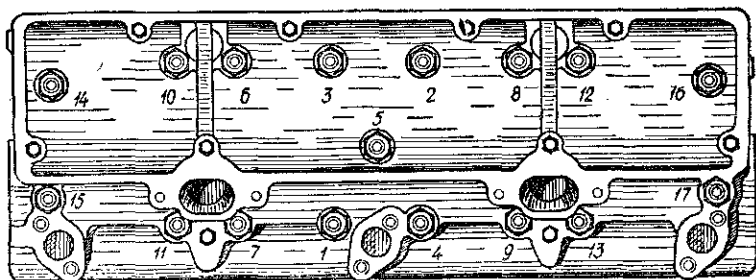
Порядок затяжки гаек крепления головки цилиндров.
